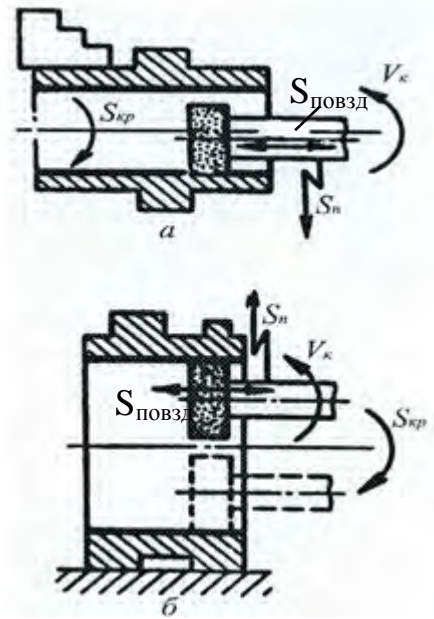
Схеми оброблення заготовок 9. на внутрішньо-шліфувальних верстатах
